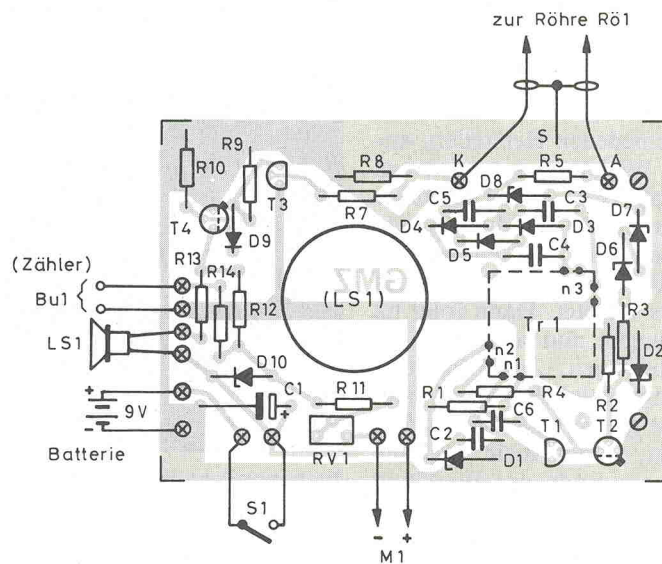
Der Widerstand R6 wird in der Zählröhrensonde untergebracht, C7 wird unmittelbar an die Meßwerkanschlüsse gelötet.
